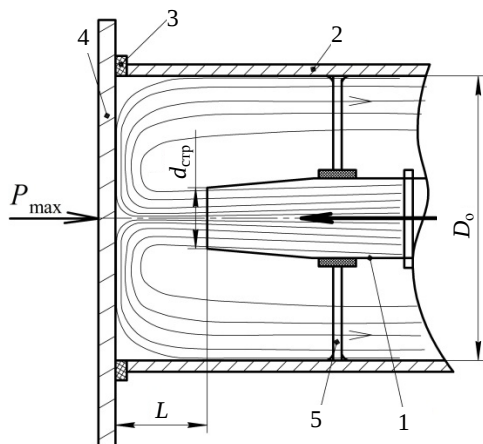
Схема струйного устройства для реализации процесса реверсивно-струйной очистки
